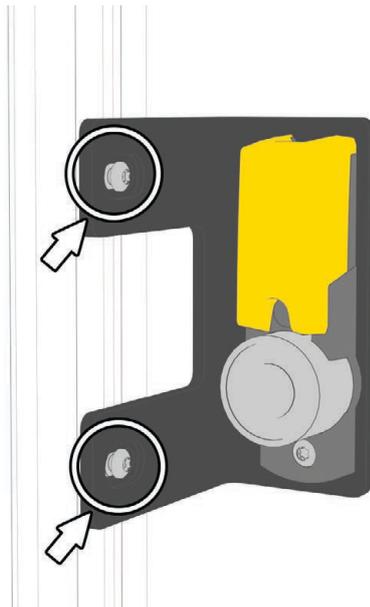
Montageplatte mit Prozesszuhalterung am Profil anbringen und Schrauben M8 x 12 mm Torx festziehen.
